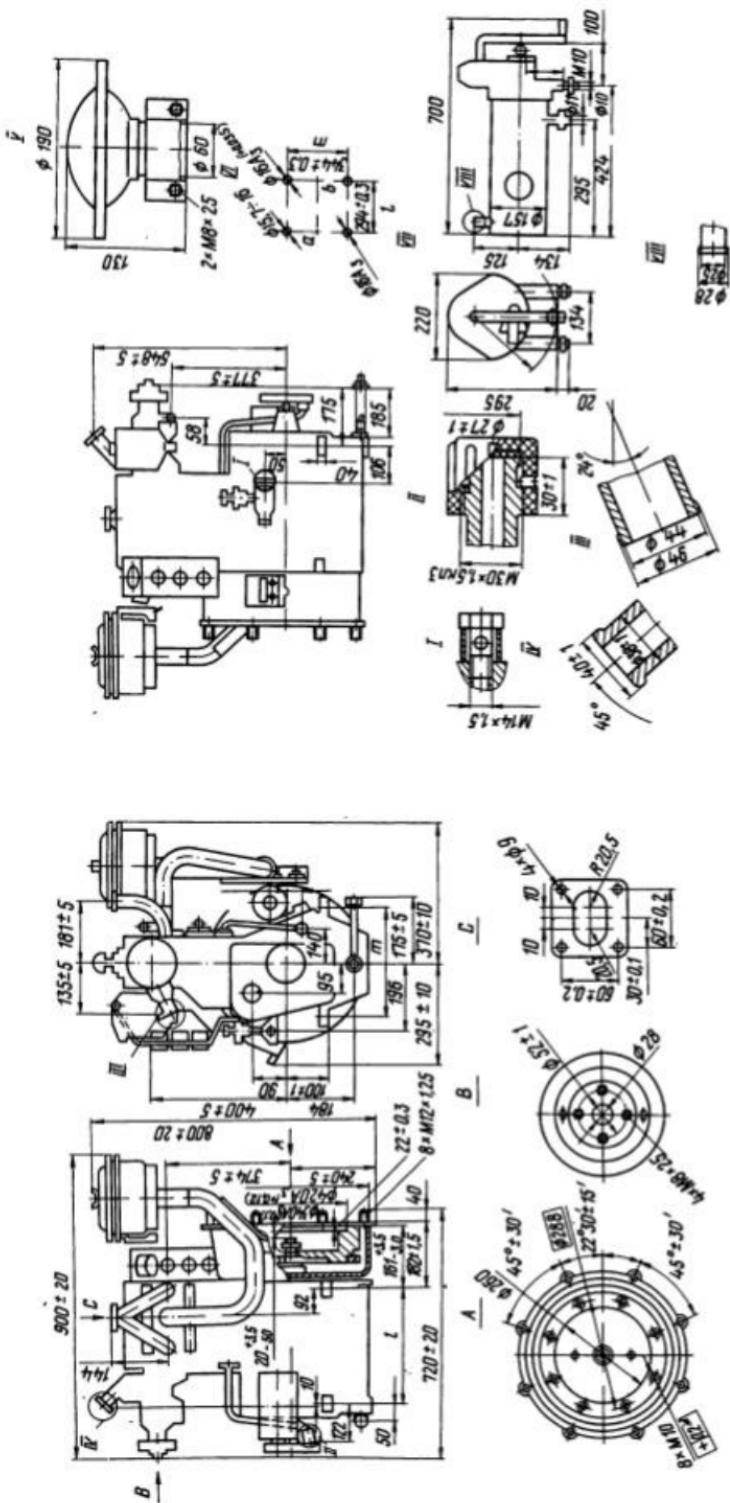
Габаритный чертеж дизеля 2Ч 8,5/11 (1Р2+10Ф):
